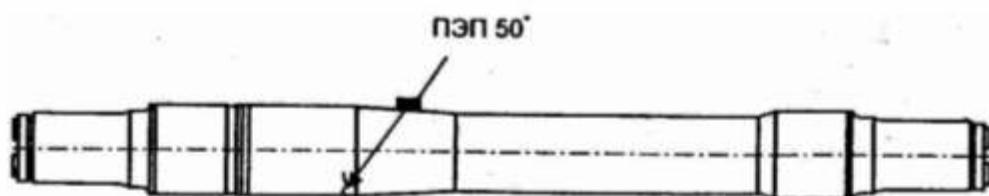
Акустическая схема контроля под ступицей колесного центра и зубчатого колеса наклонным ПЭП с цилиндрической поверхности средней части оси
